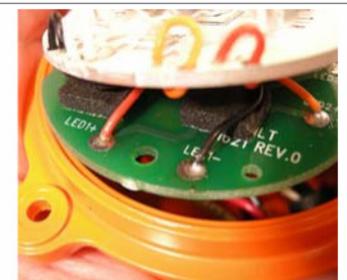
Polaritätsmarkierungen auf der PCB-Platine
